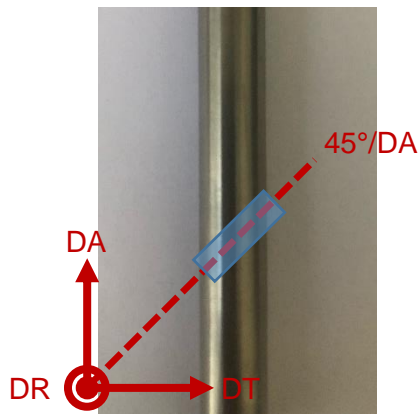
Schéma de prélèvement des éprouvettes de dilatométrie.
